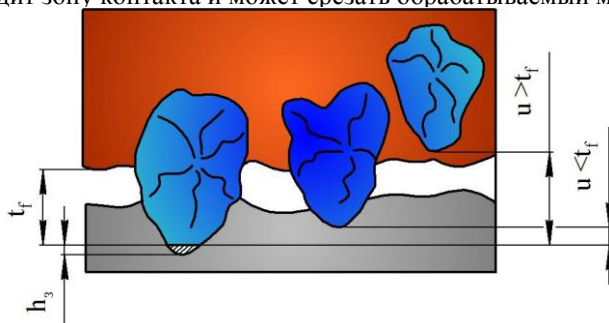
Схема зоны контакта алмазного сверла с заготовкой
